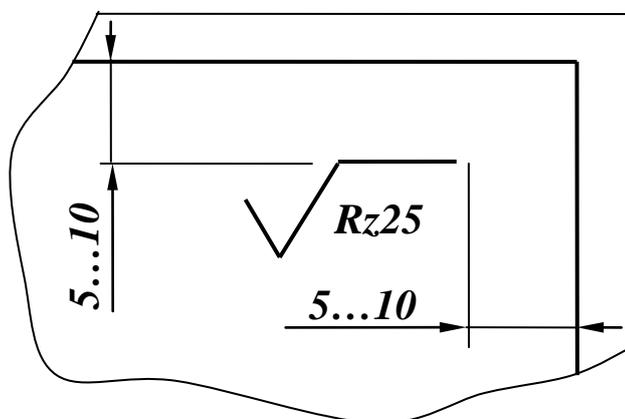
Указание шероховатости, одинаковой для всех поверхностей изделия
